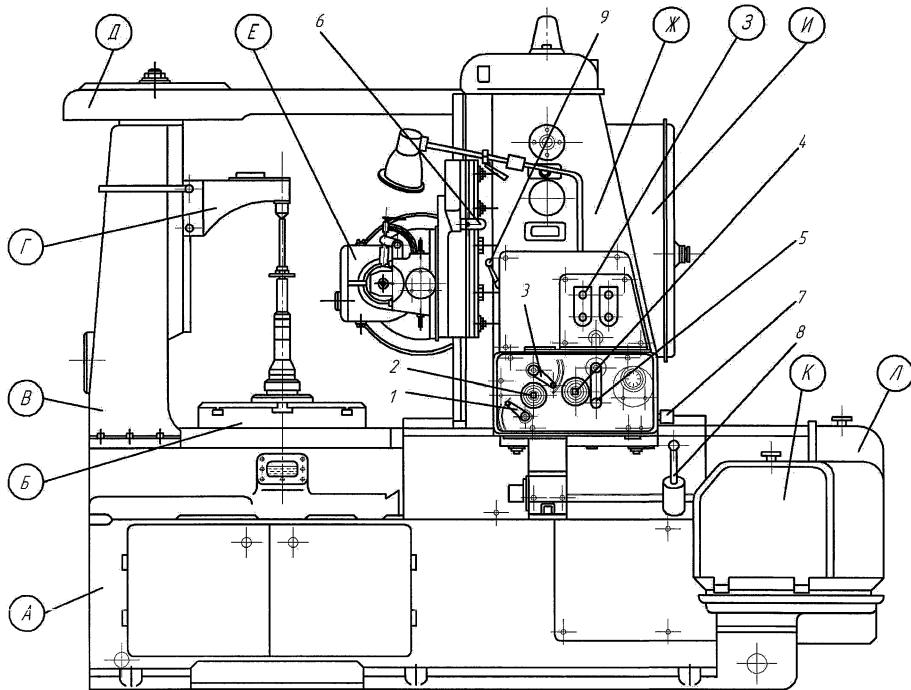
Общий вид зубофрезерного станка модели 5Д32
